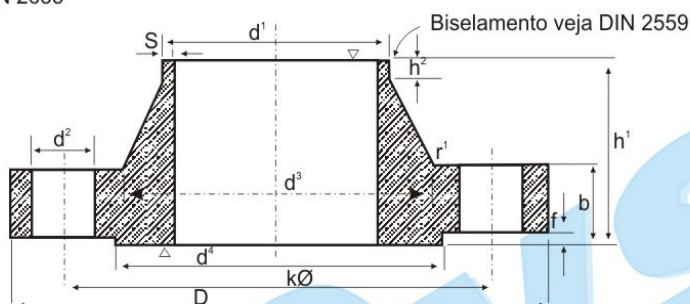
D25 - FLANGE COM PESCOÇO (DIN)
